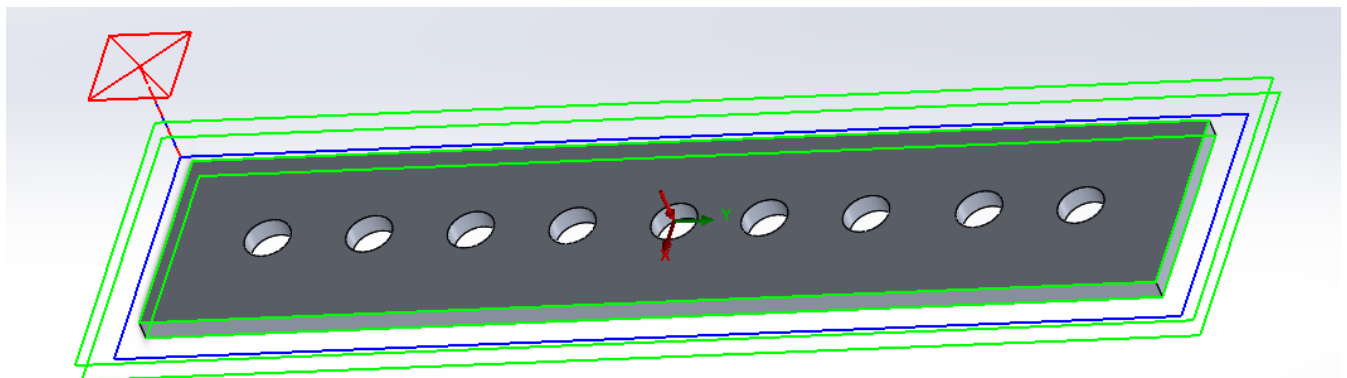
Траєкторія руху кінцевої фрези Sandvik 2P340-0500-PA 1630
